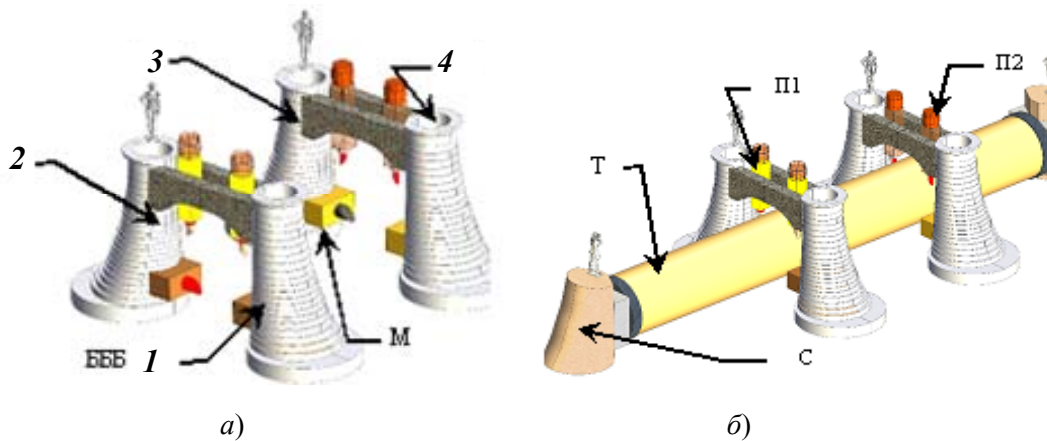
Квадруполь из четырех бионических бетонных башен (БББ – 1–4) с аддитивными и субтрактивными модулями М (*а*) и схема токарной обработки детали-трубы Т в квадруполе (*б*): С – подвижная стойка для трубы; П1, П2 – пара динамических порталов
